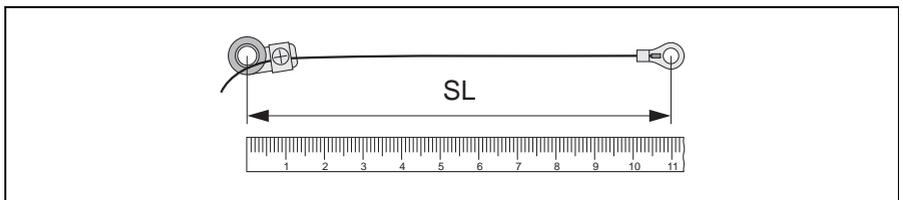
Fixierteil (a) und Kabelschuhe (b) mit einem Abstand entsprechend der Schnurlänge (SL)
